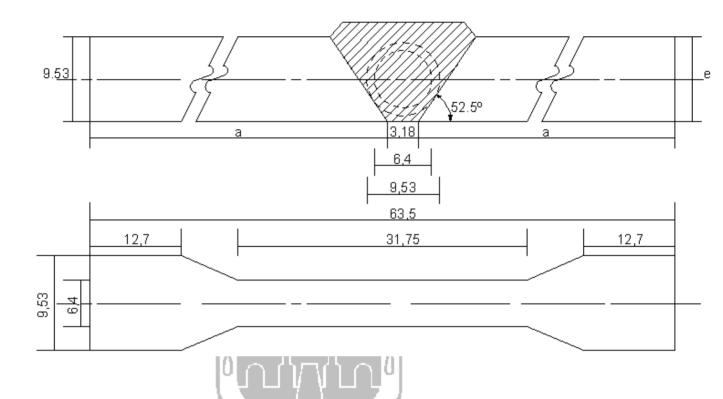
Forma de obtener el espécimen longitudinal para la prueba de tensión de la soldadura metal puro.
